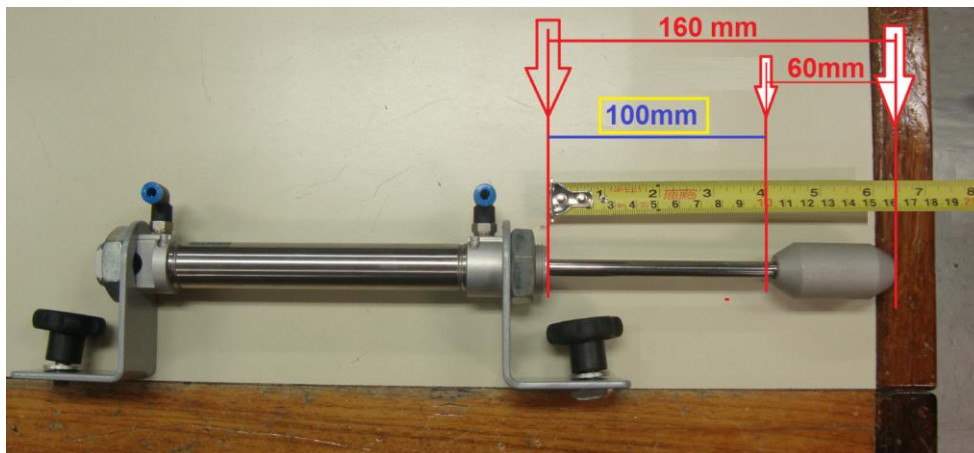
Cálculo do comprimento da haste do cilindro pneumático
